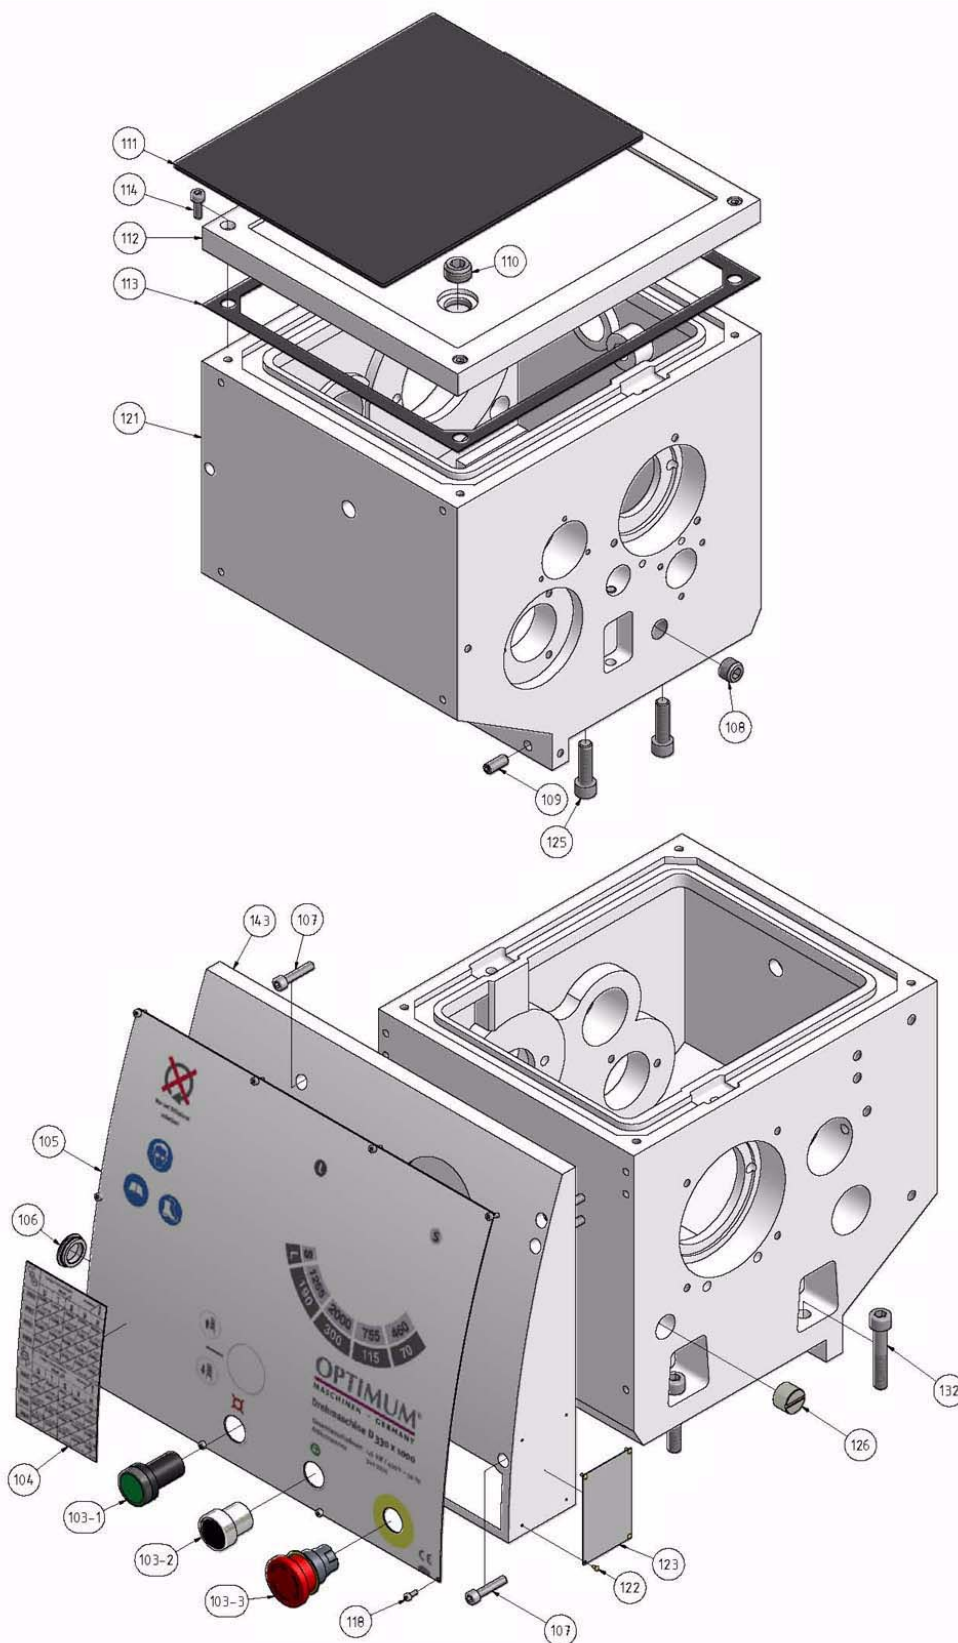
Getriebe Spindelstock 1-6 - Headstock gear 1-6
